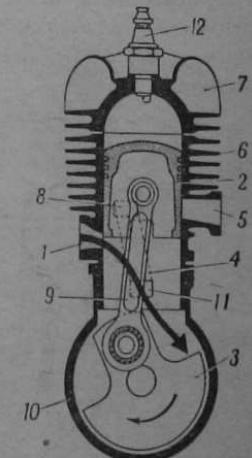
Схема рабочего цикла двухтактного двигателя — движение поршня вверх:
